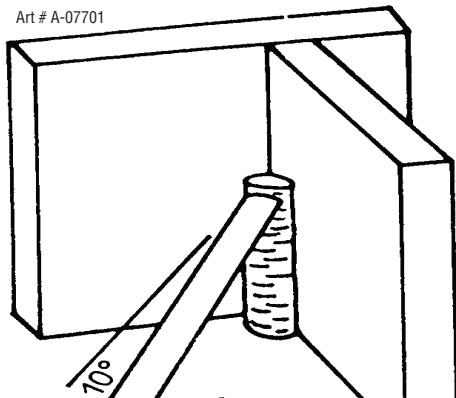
Soudure d'angle verticale à cordon unique
